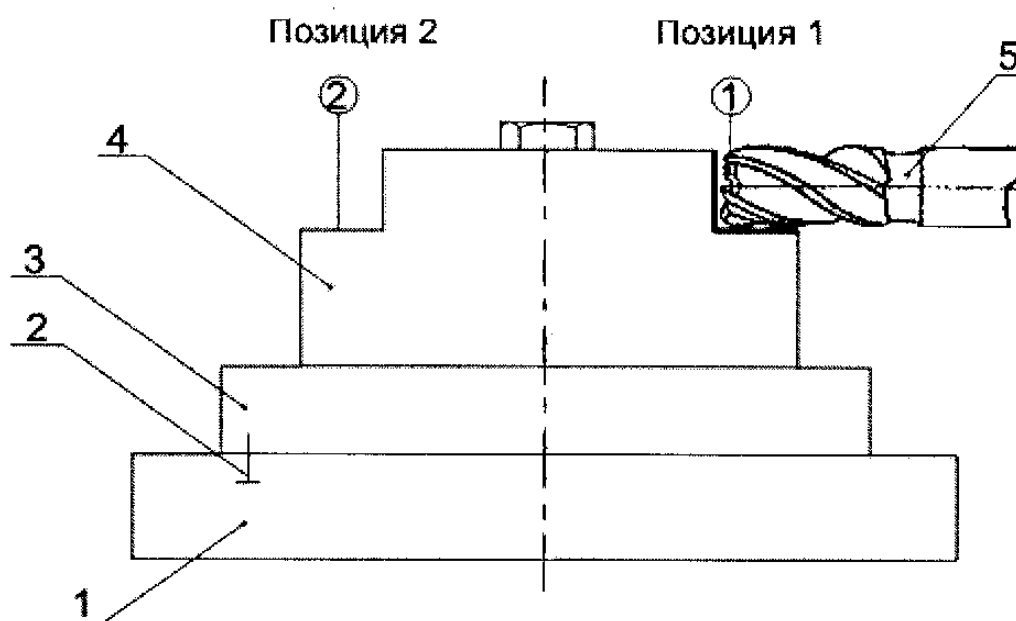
Схема обработки уступов на заготовке в специальном приспособлении на горизонтально-фрезерной операции: 1 – основание приспособления; 2 – фиксатор; 3 – поворотная часть приспособления; 4 – заготовка; 5 – фреза концевая
